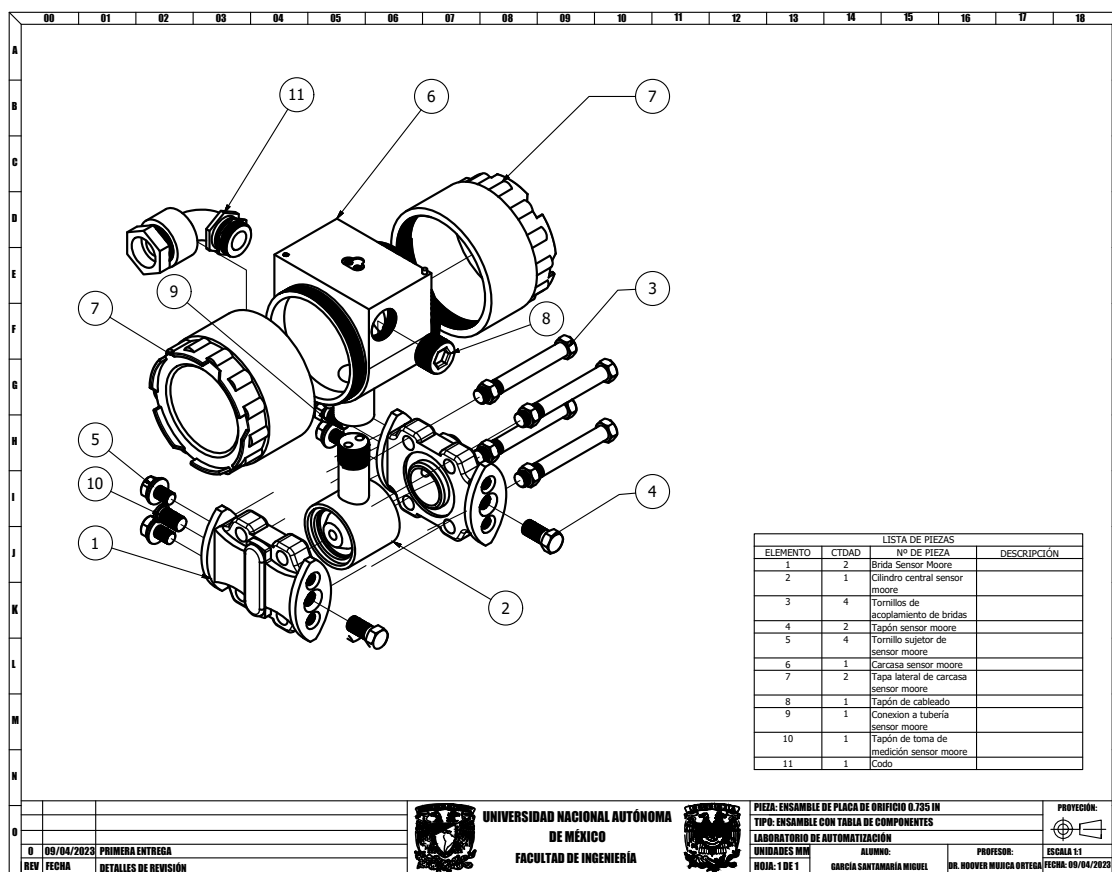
Ensamble explosionado y tabla de componentes de sensor de presión diferencial moore
